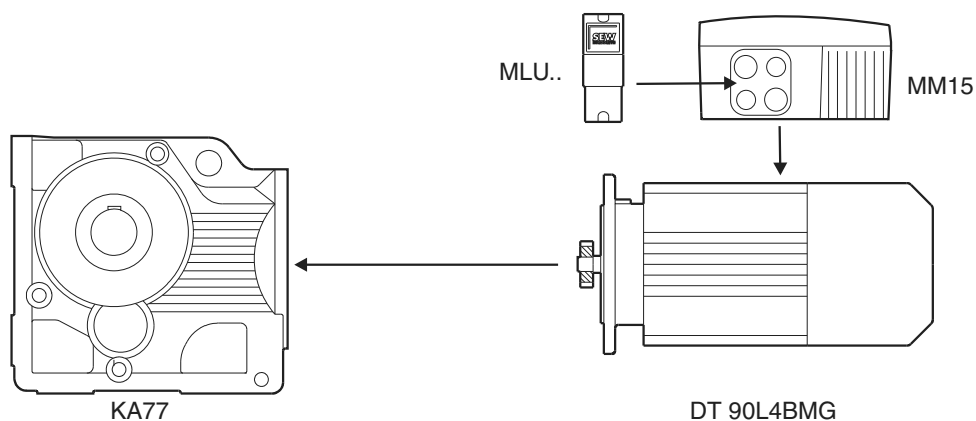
Exemplo de designação de um moto-redutor MOVIMOT®
